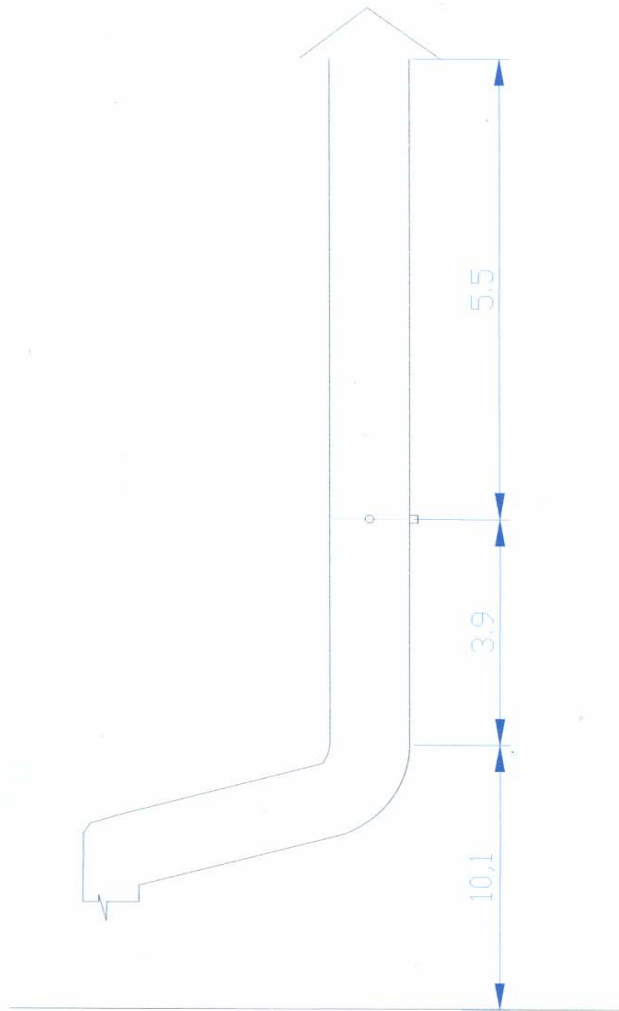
Chimenea cemento 1, sección transversal, longitud en cm.
